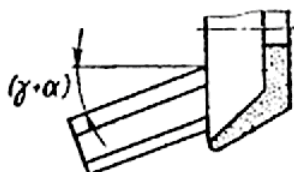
Схема заточки призматического фасонного резьбового резца по передней поверхности
